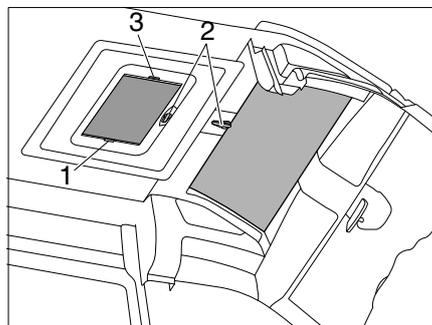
Kurbelhub-Dachhaube mit SkyRoof®
